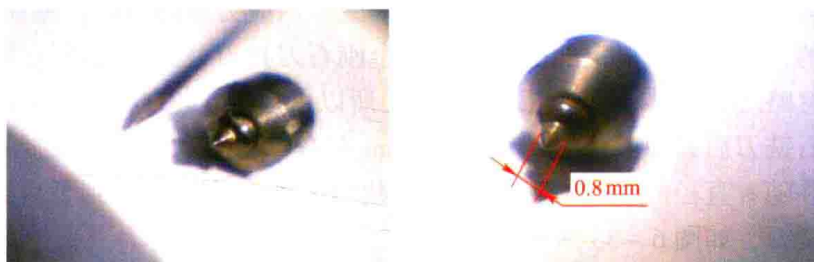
减径滚磨后的焊接刀杆式圆柱立铣刀
